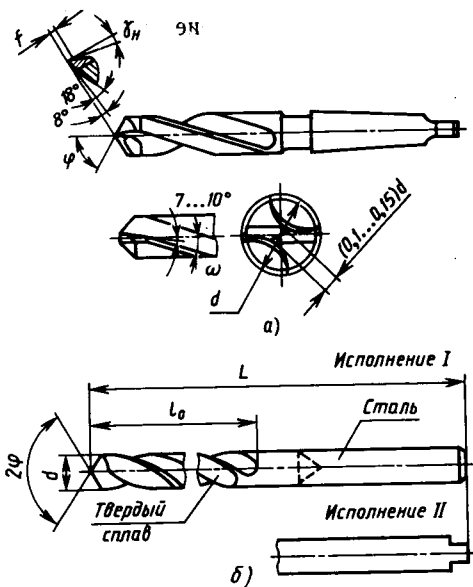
Сверла, оснащенные пластинами из твердого сплава
